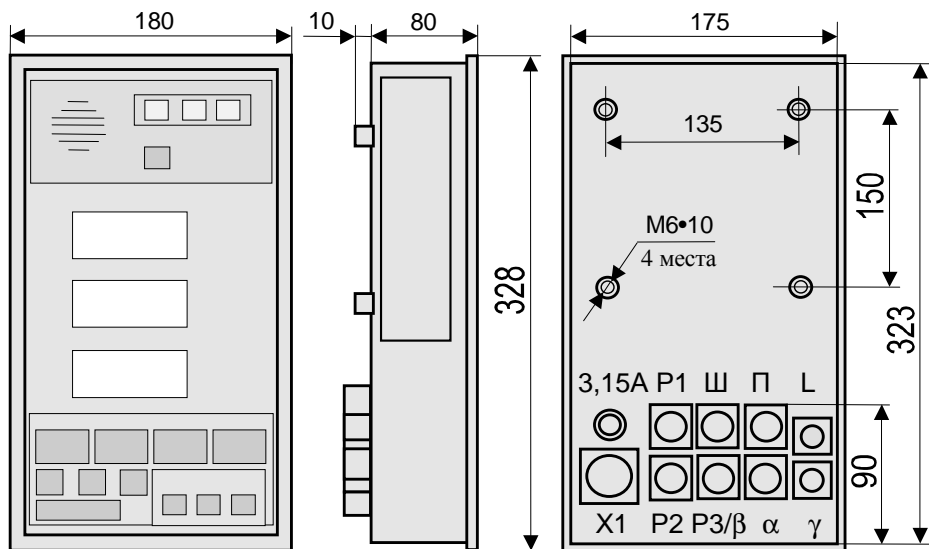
Габаритные и присоединительные размеры БОДа
